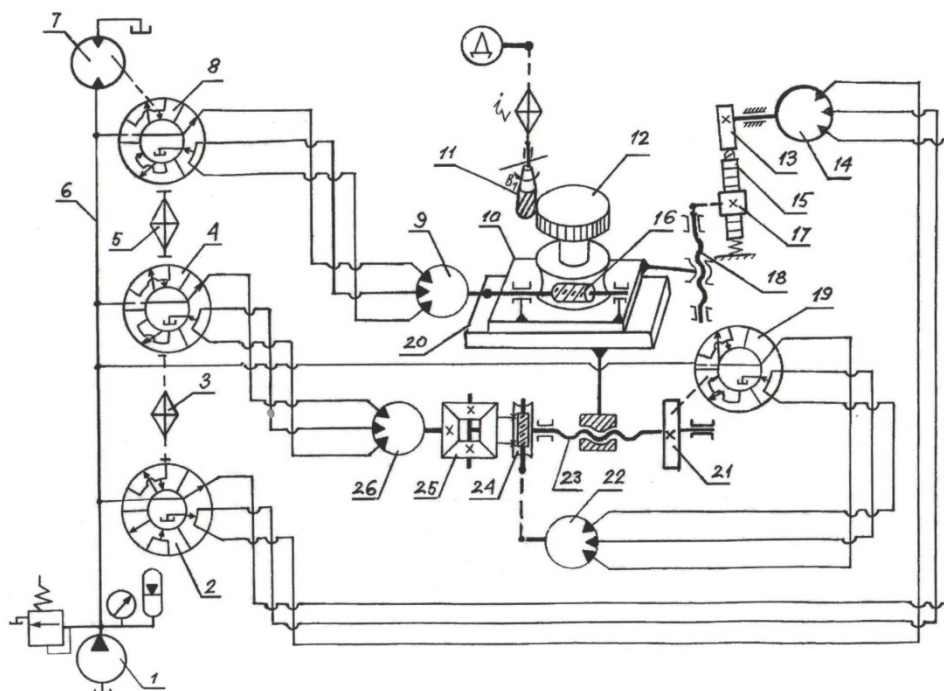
Структурная схема копировально-фрезерного станка с гидравлическими формообразующими связями для обработки рабочей поверхности дисковых кулачков
